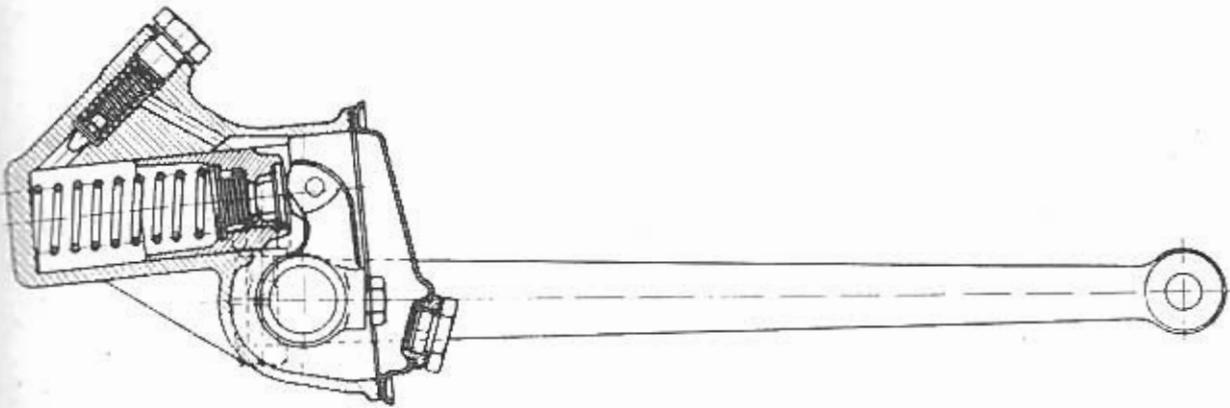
Hydraulischer Stoßdämpfer der Hinterrachse
